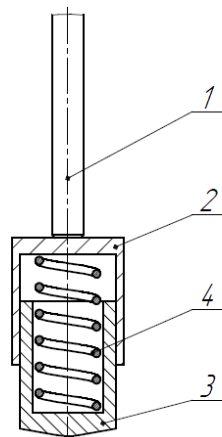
Пружинний механізм: 1 – шток; 2 – верхній стакан; 3 – нижній стакан; 4 – пружина [3].
